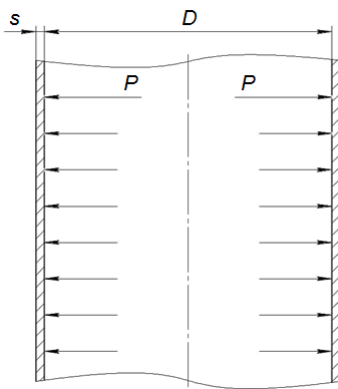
Схема до розрахунку товщини стінки циліндричної обичайки
